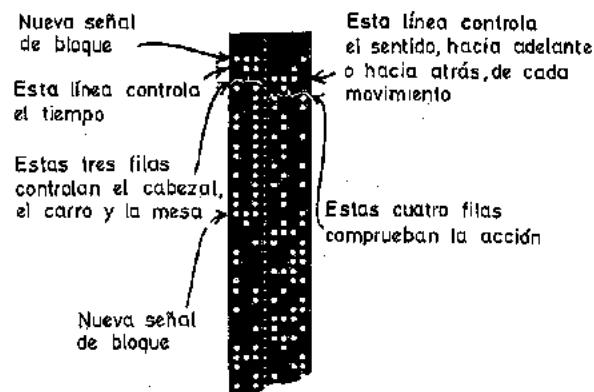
Fragmento de cinta de control típica (American Machinist, McGraw-Hill, Inc.)
